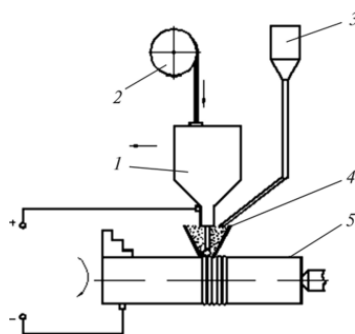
Принципиальная схема автоматической электродуговой наплавки деталей под флюсом: 1 – наплавочный аппарат; 2 – кассета с проволокой; 3 – бункер с флюсом; 4 – электродная проволока; 5 – наплавляемая деталь
